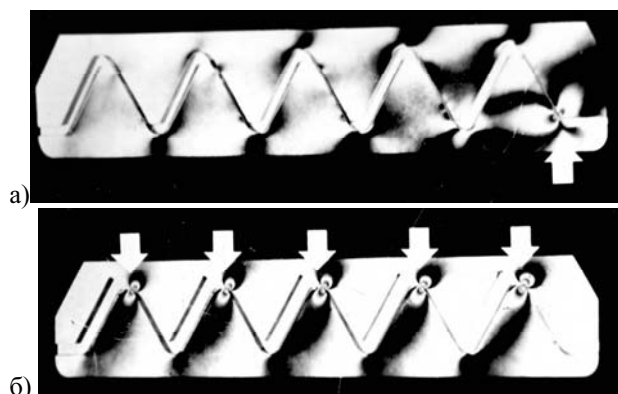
Картини изохром: а – стандартної різьби; б – "EMUGE-SPIRALOCK" різьби
